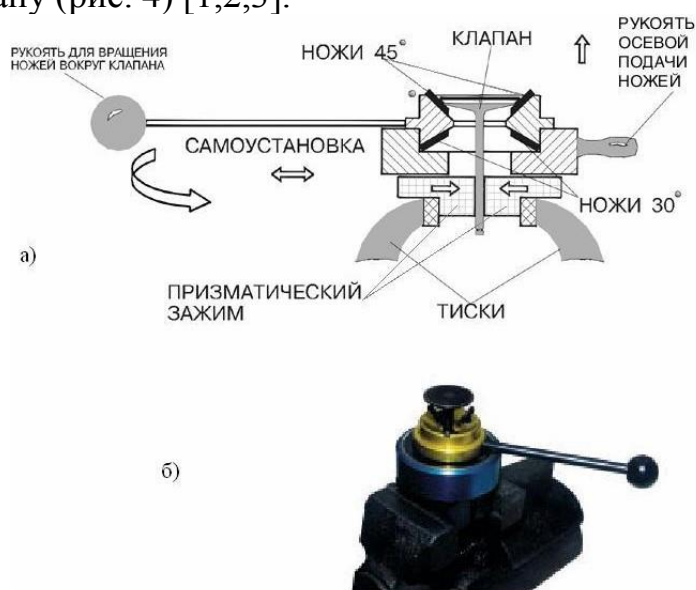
Ручной инструмент GIZMATIC для ремонта фаски клапанов: а – схема инструмента; б – внешний вид в тисках
